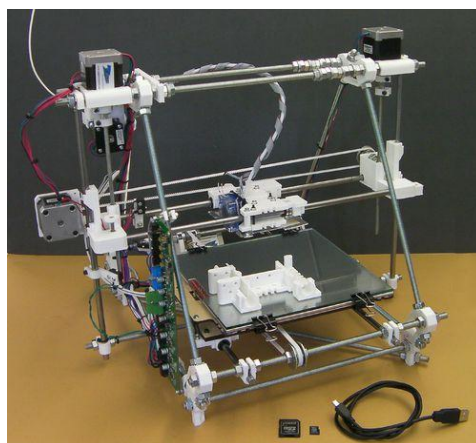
3D Printing (zdroj: <http://www.custompartnet.com/wu/3d-printing>)
